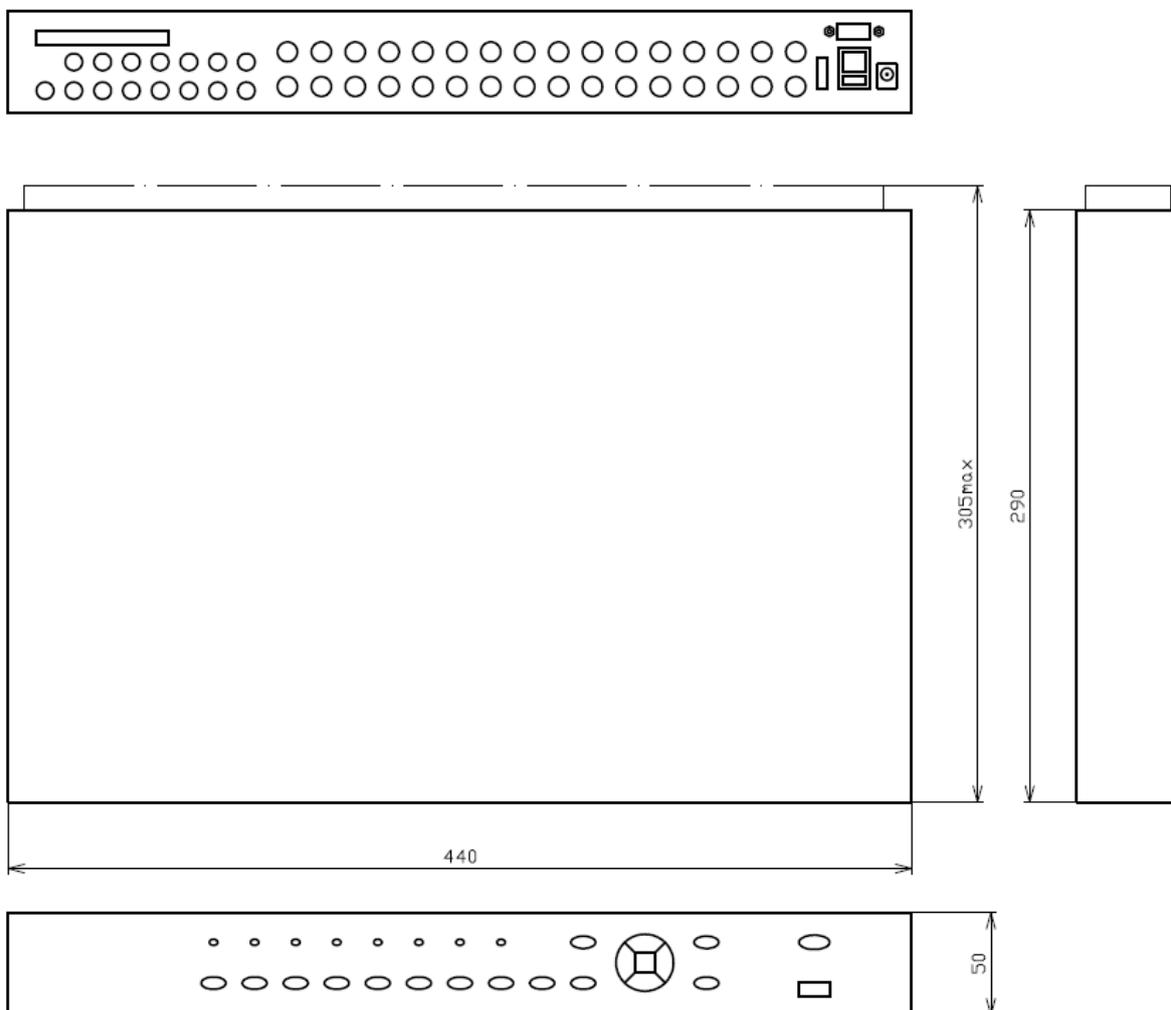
Габаритный чертеж ИВМ-8032.
